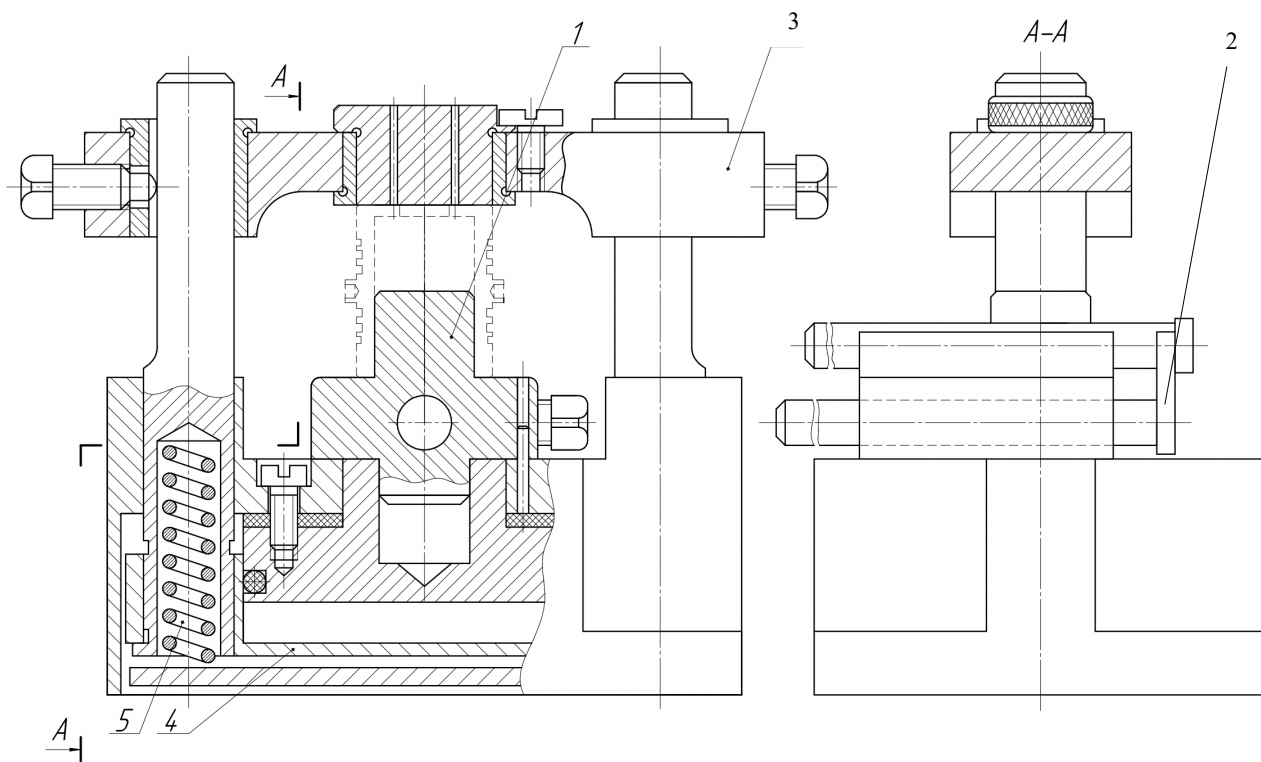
Кондуктор с пневматическим зажимом для сверления отверстий:
